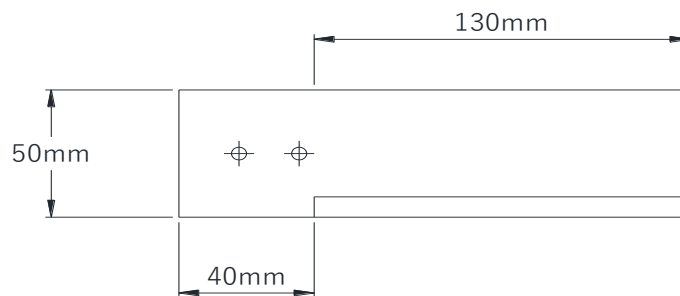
Dimensiones geométricas de la cuchilla de corte
